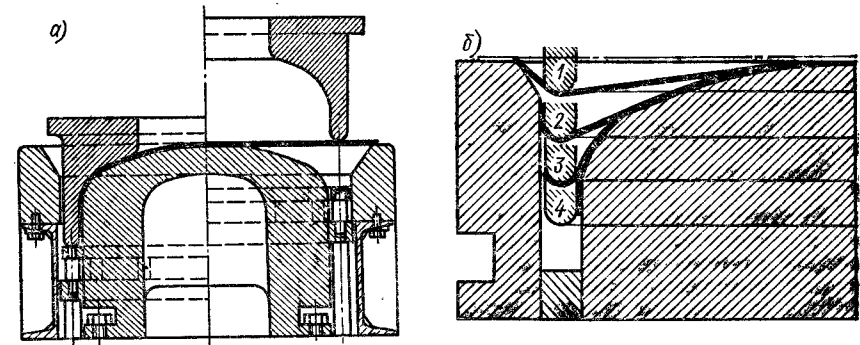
Вытяжка с двойным перегибом заготовки: а — схема штампа; б — последовательность деформации (1—4)
